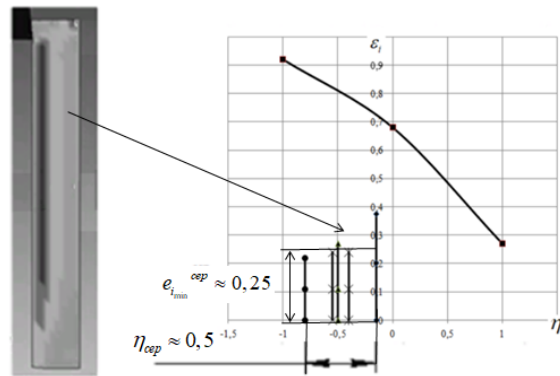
Шляхи деформування, що характерні для вісі заготовки при фіксованому натягові заготовок із сплаву W-Ni-Fe при різних значеннях кута нахилу матриці.
